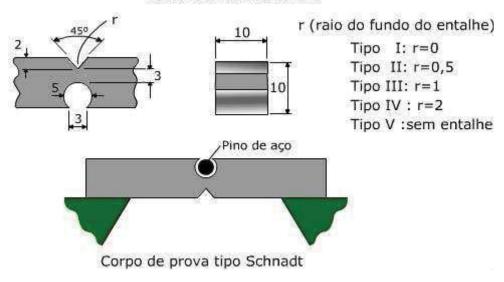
Ilustração Fonte: (CIMM, 2008).
